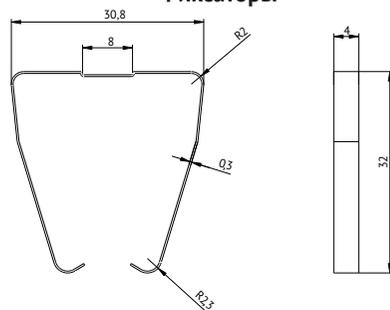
Габаритные, установочные присоединительные размеры фиксатора реле OptiRel 55-H1
